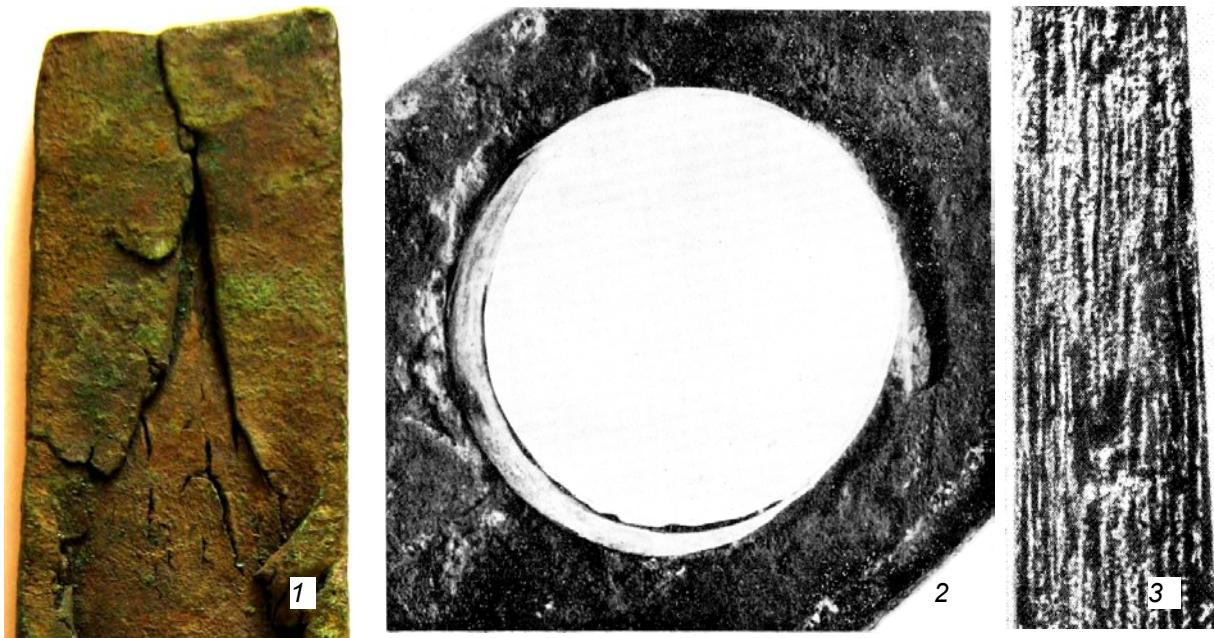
Металлические изделия со следами сварки, кузнечной ковки и сработанности
